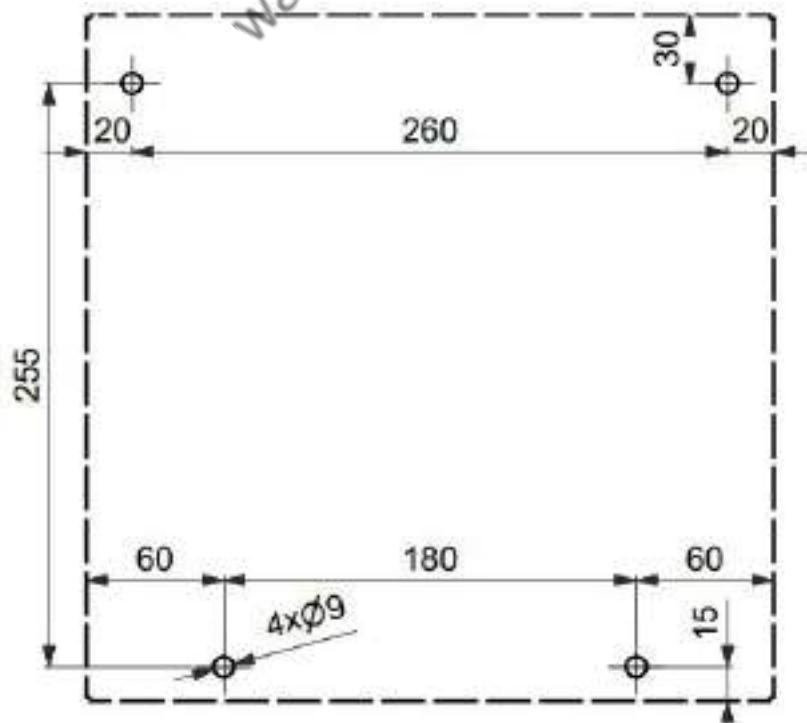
Размеры для сверления отверстий для укрепления УФ шкафа
